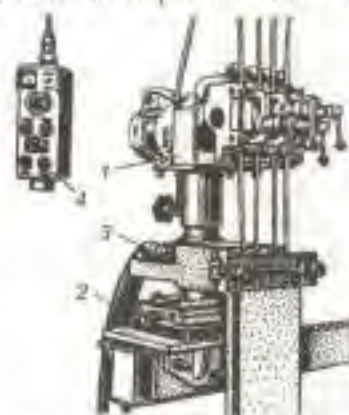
Апарат А-1304 для електрошлакового зварювання плавким мундштуком:
